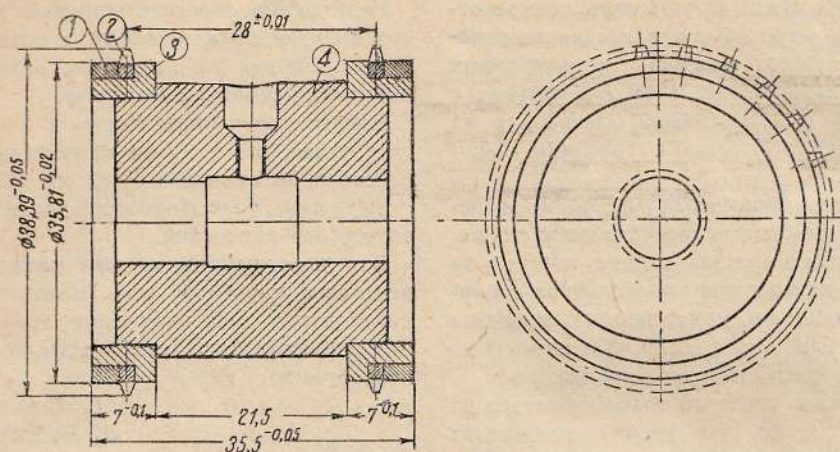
24-зубый барабан системы Киреева с запрессованным зажимным кольцом
